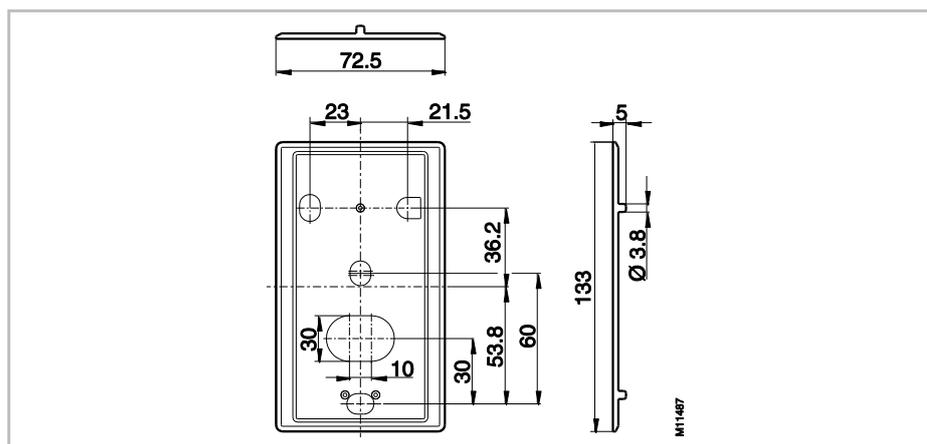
Dimensions de la plaque de protection (toutes les dimensions sont en mm)
